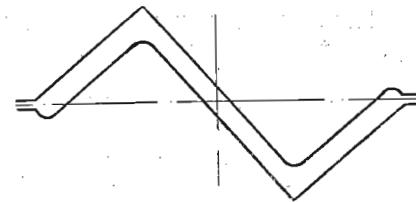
Чистовой калибр для прокатки зетового профиля с выпрямлением полок
